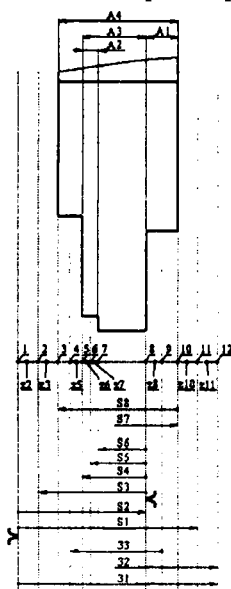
Размерная схема техпроцесса обработки детали «Фланец»
